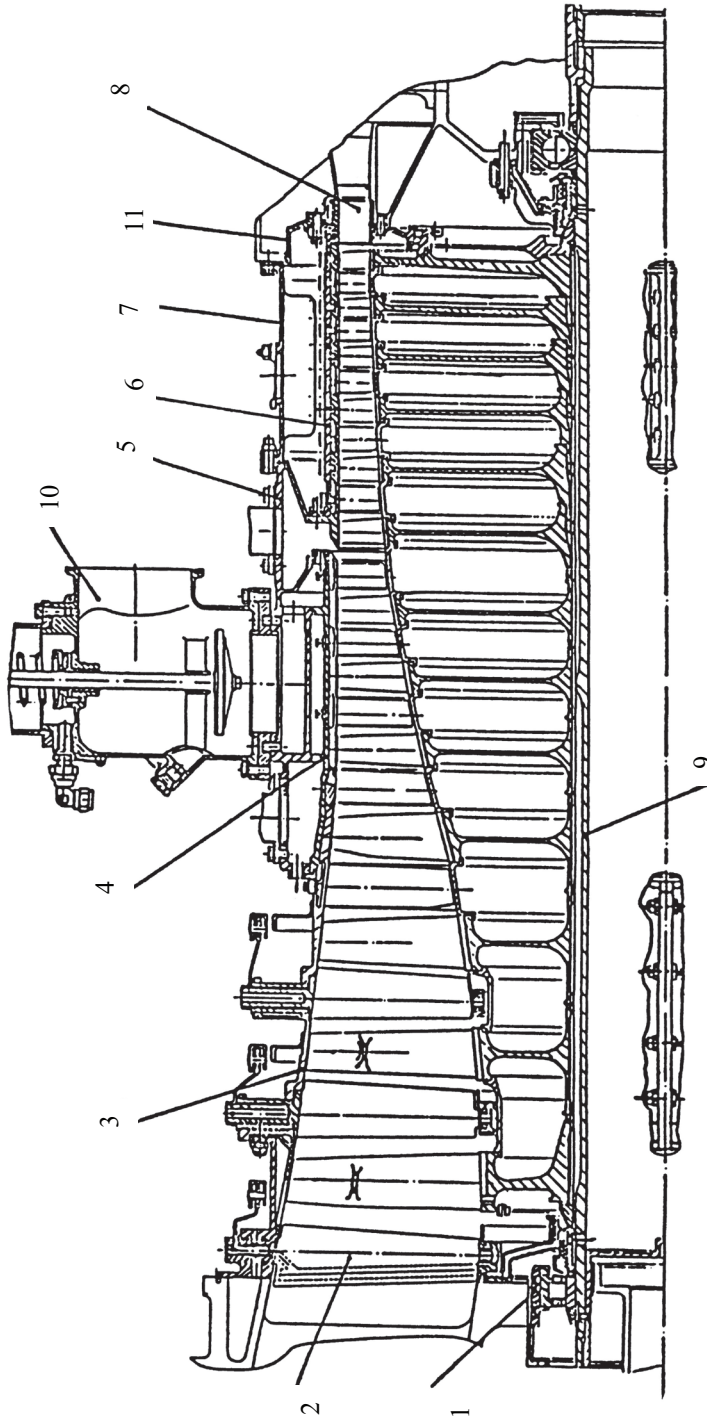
Осевой компрессор ГТД ПС-90ГП-1:
